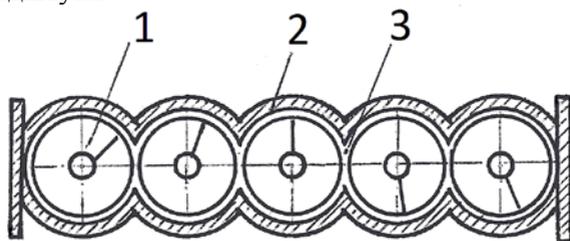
Поперечный разрез прессы: 1 – винт; 2 – кожух; 3 – пресскамера
